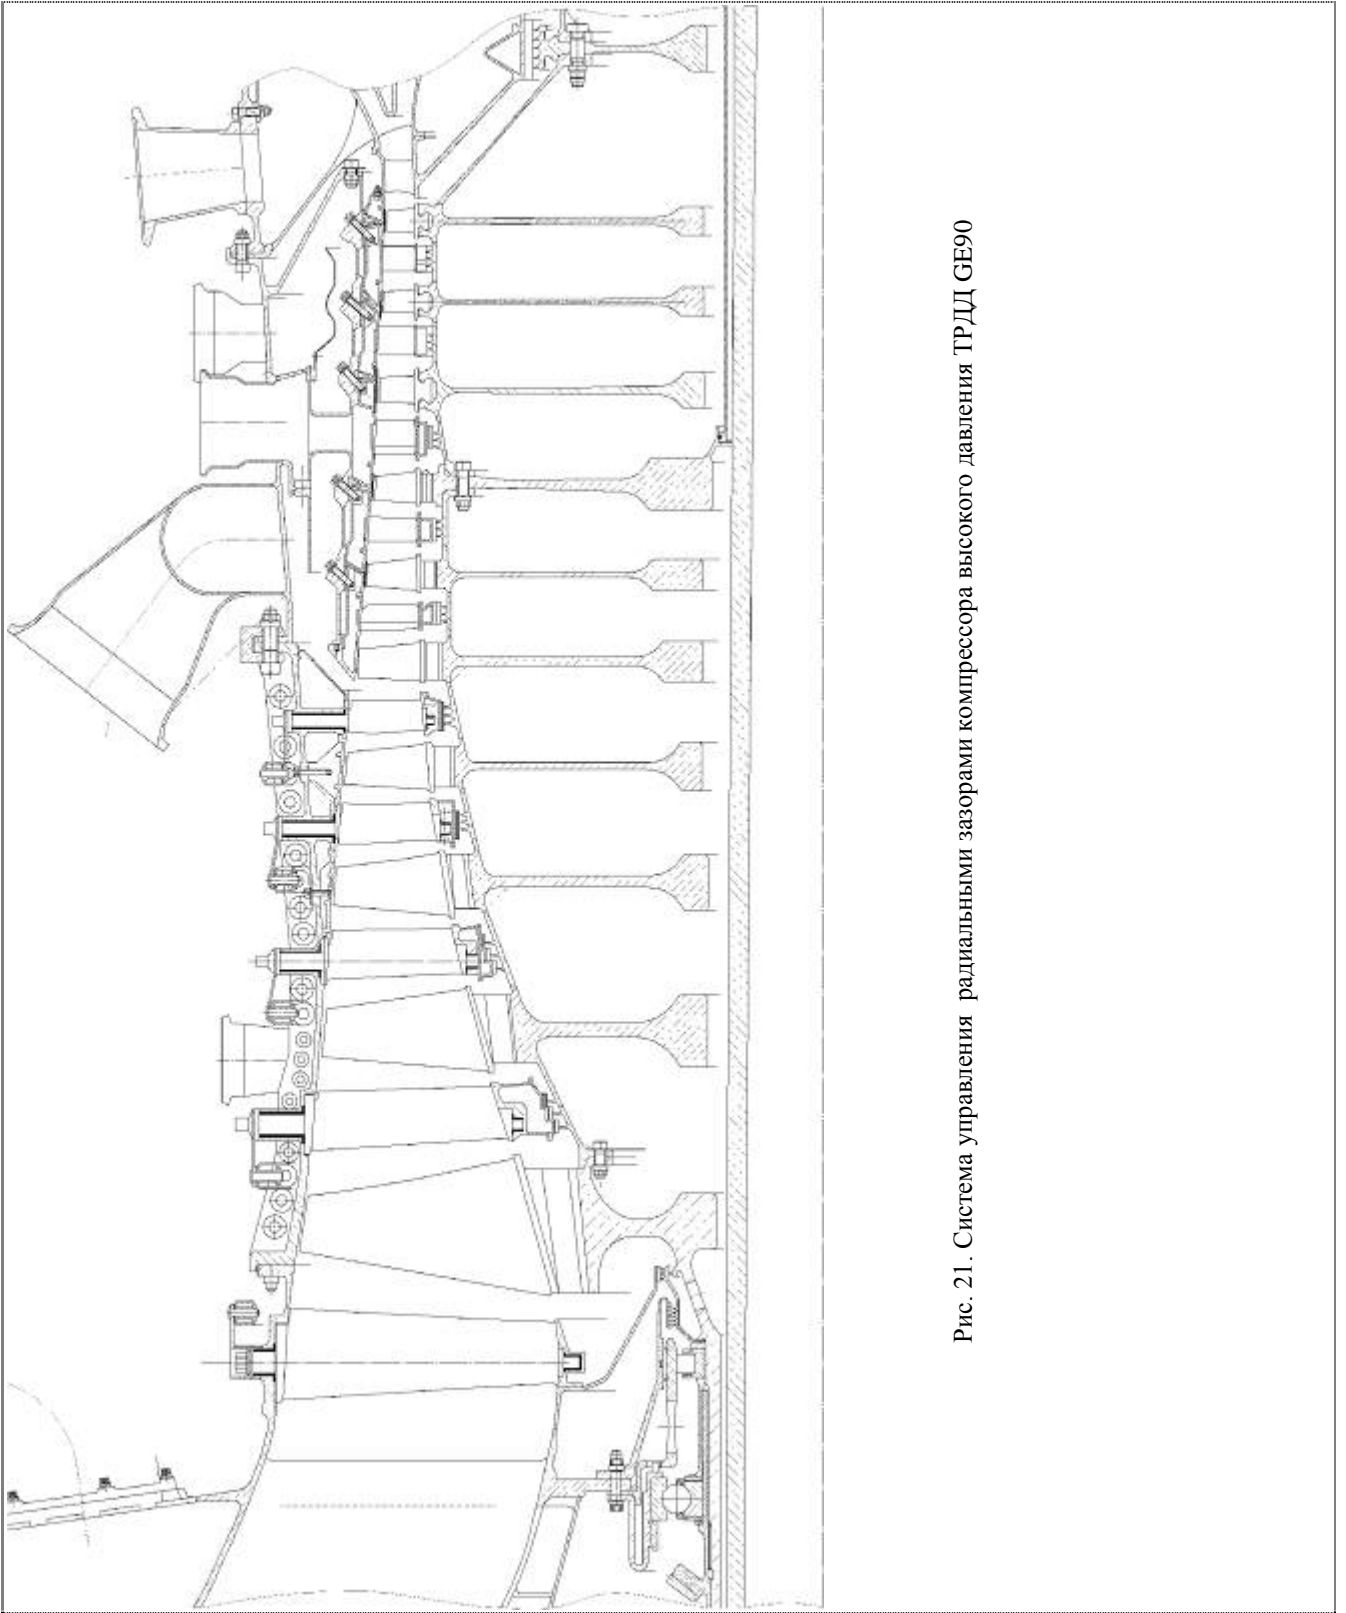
Система управления радиальными зазорами компрессора высокого давления ТРДД GE90
